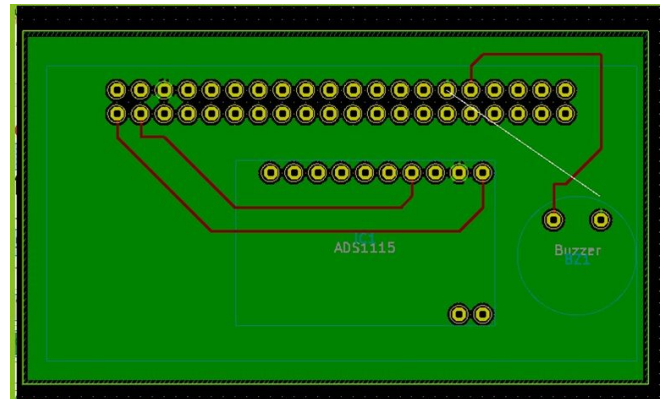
DISEÑO DE LA PCB DE LOS COMPONENTES DEL *WEARABLE
